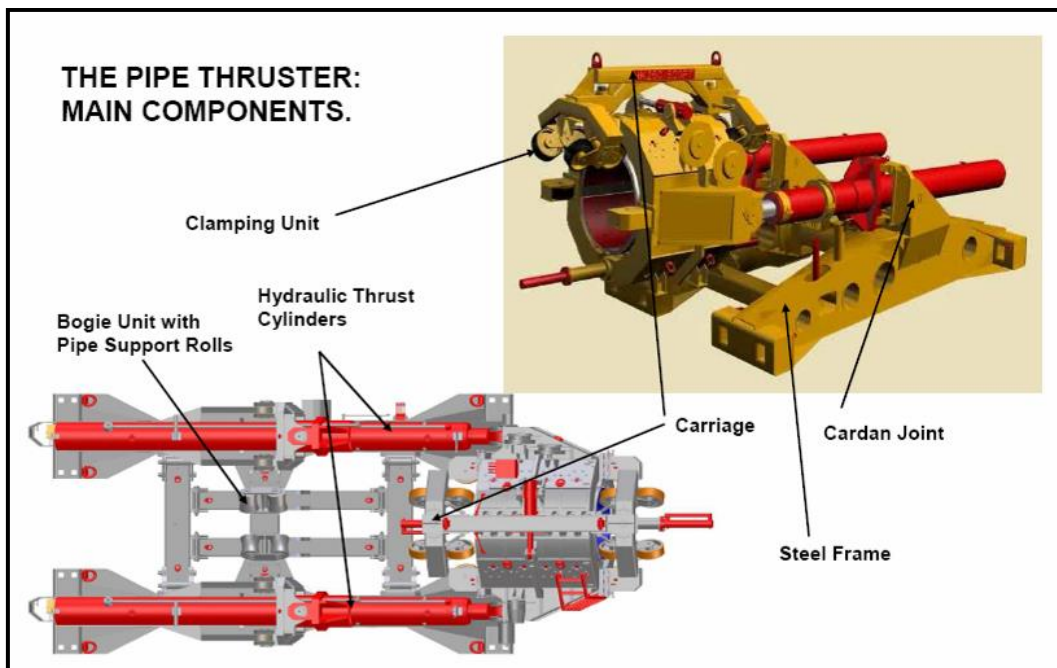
Schema di funzionamento e componenti principali del Pipe Thruster
